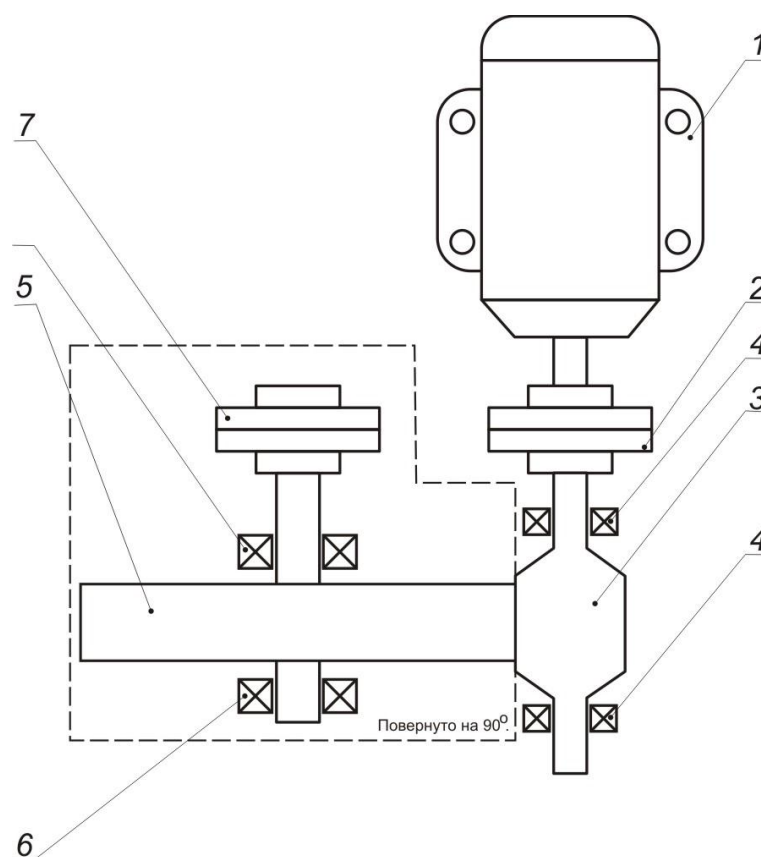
Схема червячного редуктора с электроприводом от асинхронного электродвигателя: 1 – асинхронный электродвигатель; 2 – предохранительная муфта электродвигателя; 3 - быстроходный вал-червяк; 4 – опорные подшипники быстроходного вала; 5 – тихоходный вал с надетым на него червячным колесом; 6 – опорные подшипники тихоходного вала; 7 - предохранительная муфта редуктора
